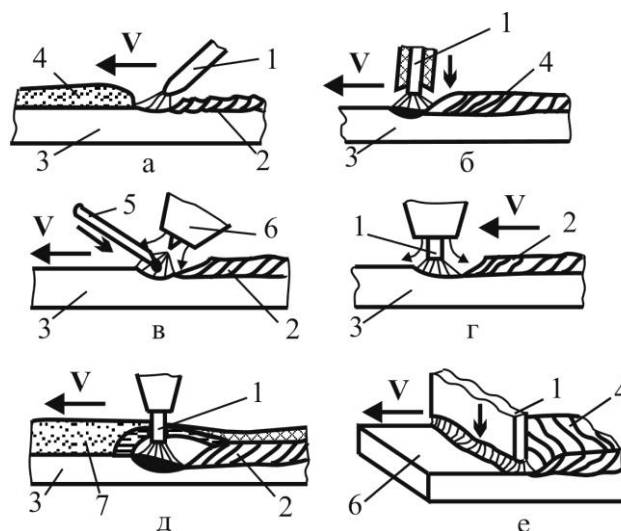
Схемы основных способов дуговой наплавки:
